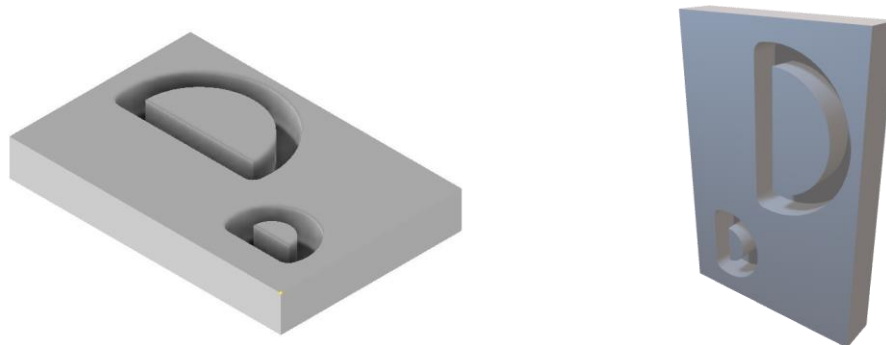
Τρισδιάστατη απεικόνιση αποστολής 47
